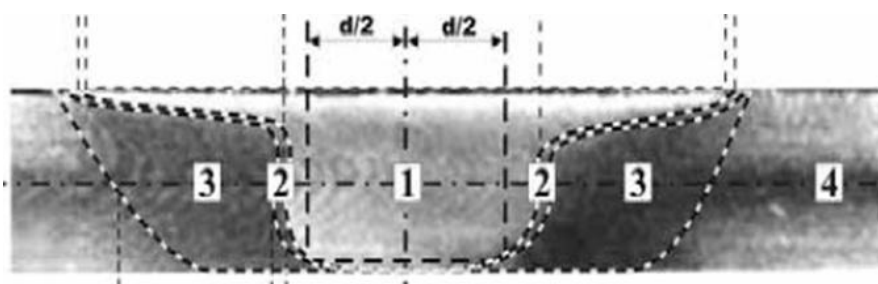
Структура металла, полученного сваркой трением с перемешиванием. 1-зона шва, 2 - зона термомеханического соединения, 3 - зона термического влияния, 4 - основной металл.
